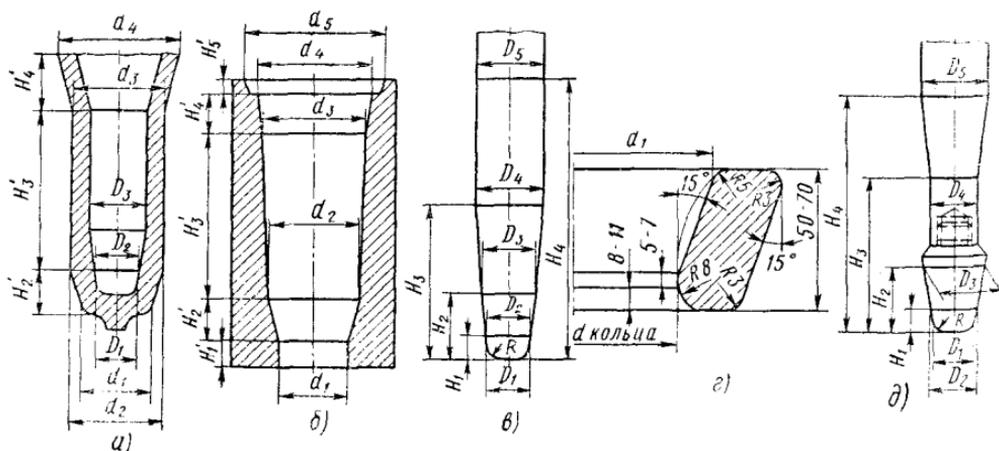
Прошивная заготовка и основные детали прошивного и протяжного штампов
